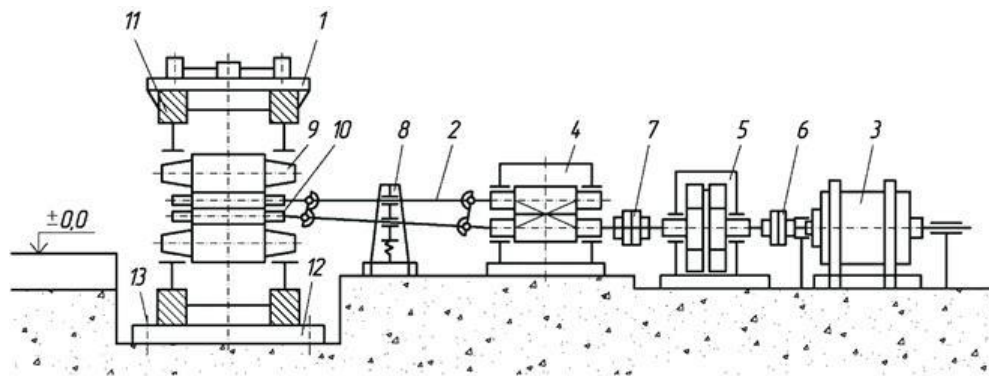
Схема главной линии четырехвалковой рабочей клетки листопрокатного стана
